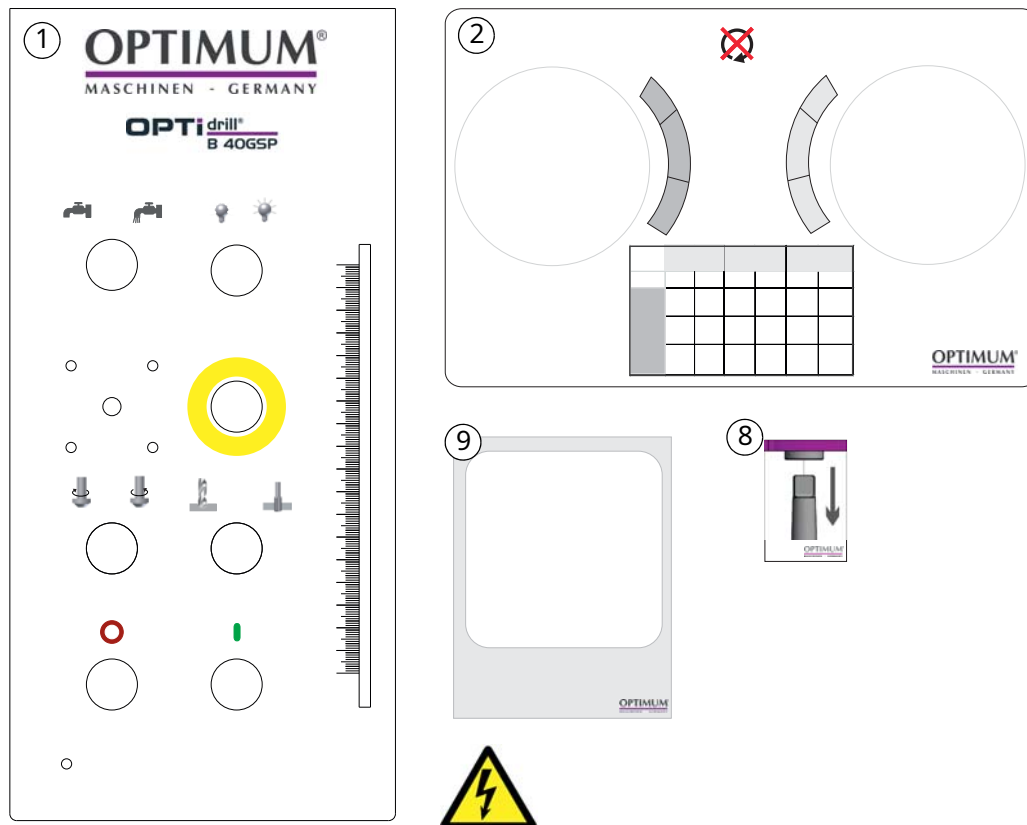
Maschinenschilder - Etiquetas para máquinas
